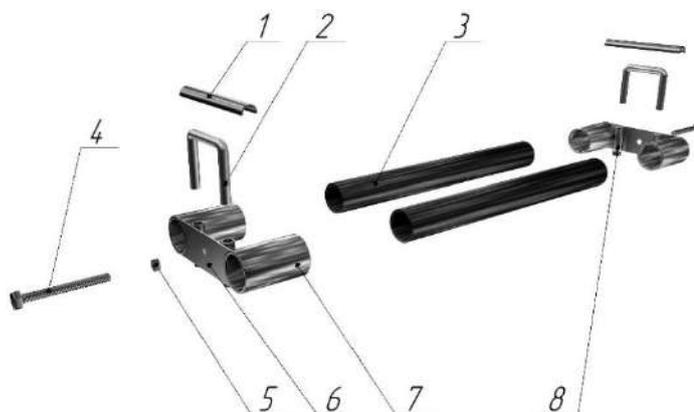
«Взрыв-схема» фаркопа: 1 – зажим, 2 - П-образная скоба, 3 - труба соединительная, 4 – болт, 5 – гайка, 6 - пластина соединительная, 7 - патрубок, 8 - втулка зажимная
